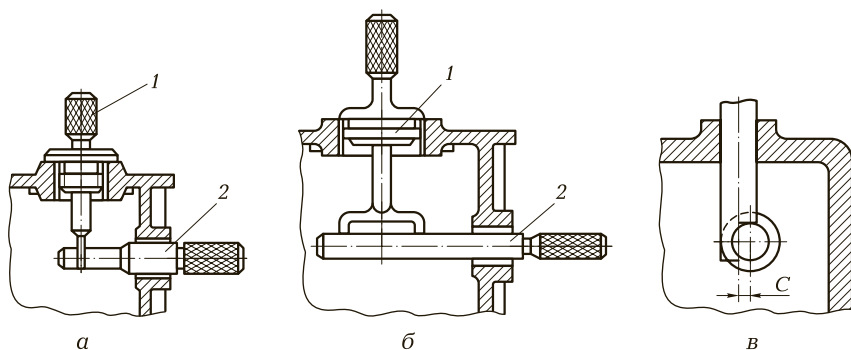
Схема контроля расположения осей отверстий под валы зубчатой передачи с помощью калибров:
